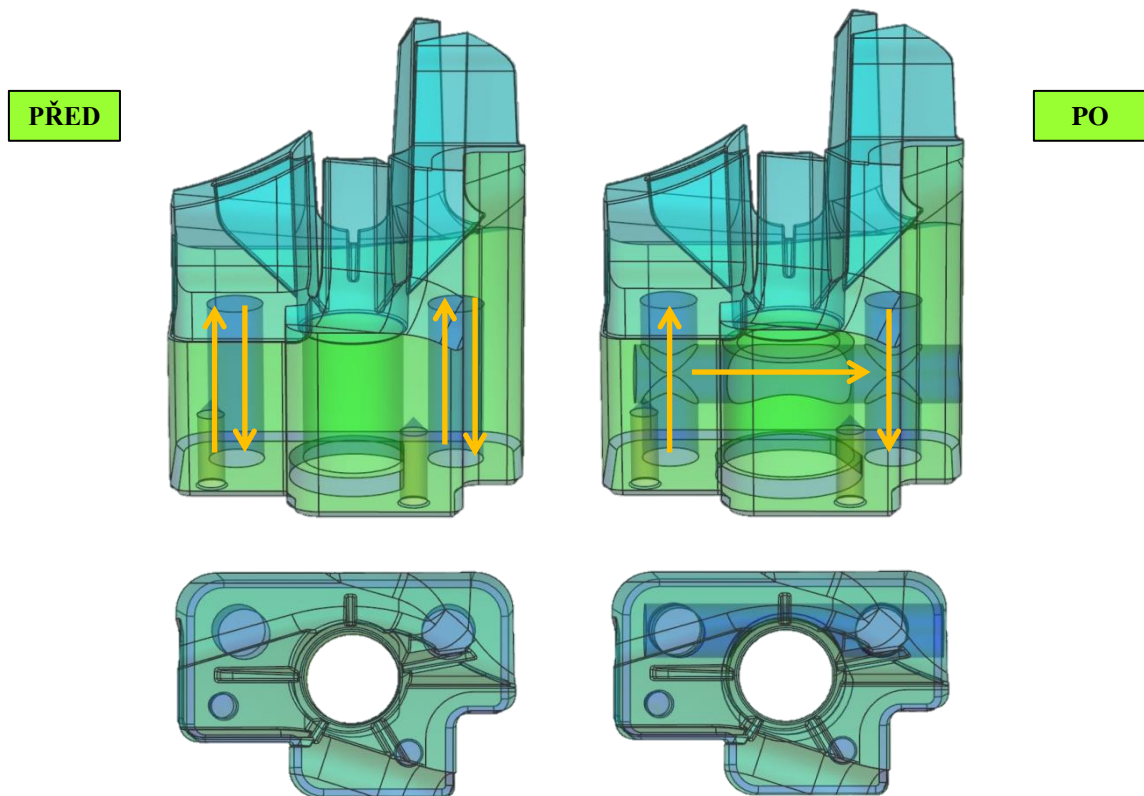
Umístění Insertu_L2 ve Slideru_L [18]
